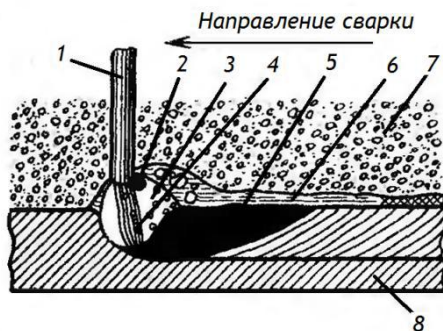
Сварка под флюсом, где 1 – сварочная проволока, 2 – образующаяся капля, 3 – газовый пузырь, 4 – дуга, 5 – сварочная ванна, 6 – расплавленный флюс, 7 – нерасплавленный флюс, 8 – изделие
